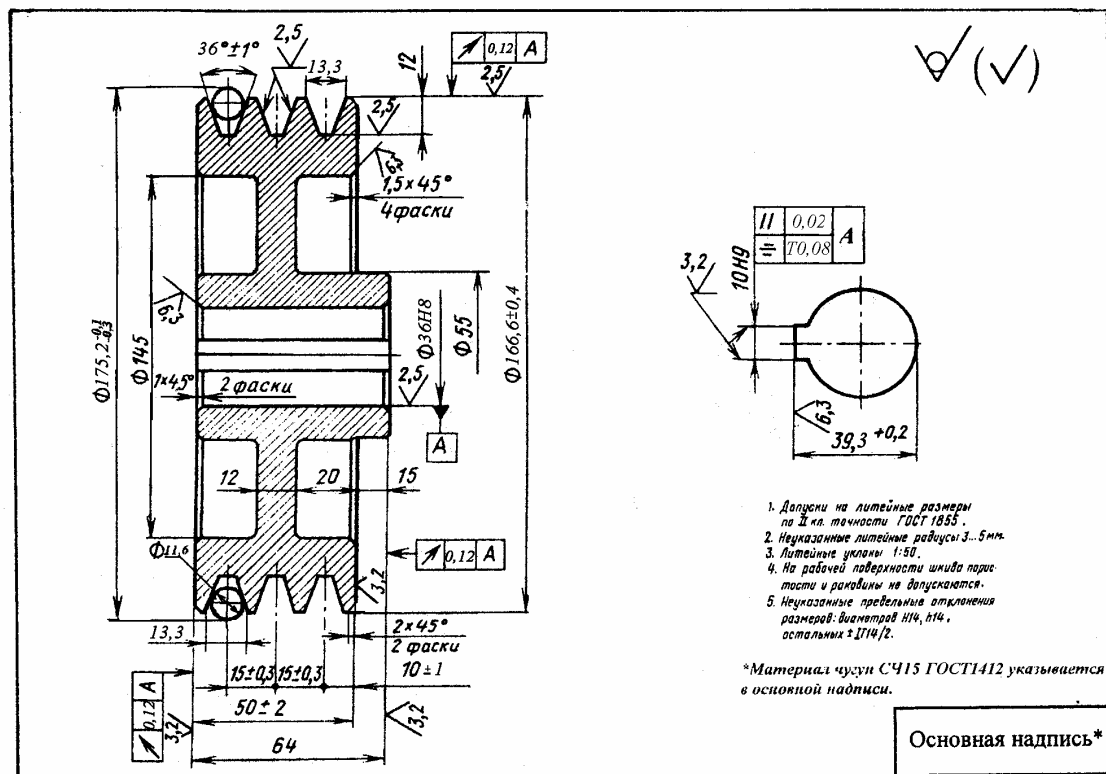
Рабочий чертеж шкива клиноременной передачи
